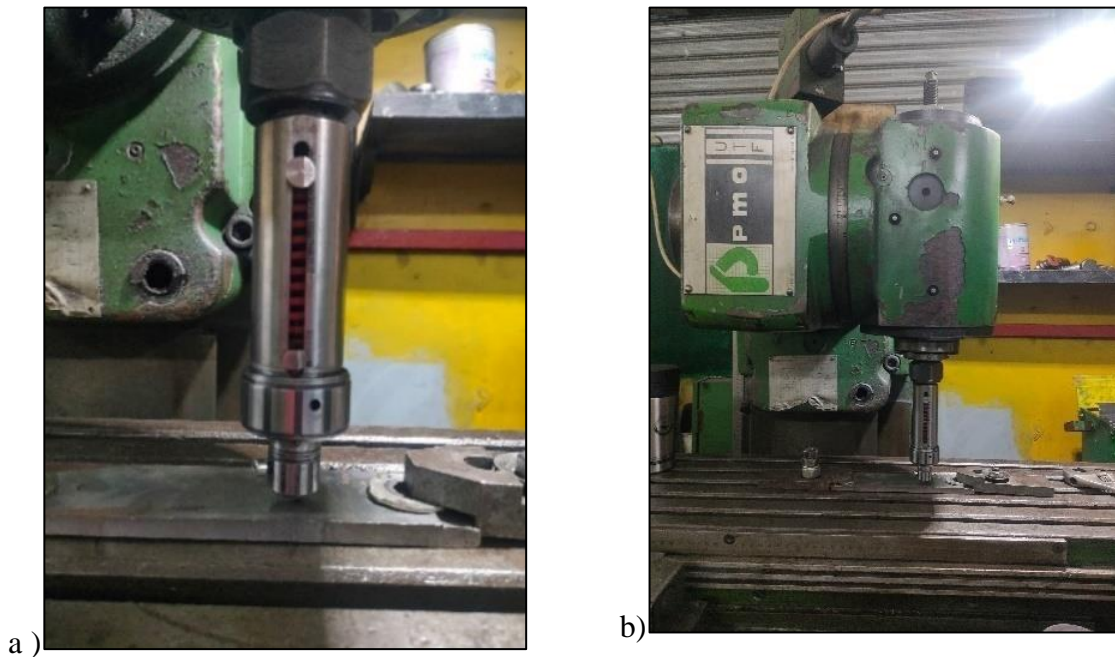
Montage du dispositif de brunissage et de la pièce sur la machine a) Montage du dispositif, b) Fraiseuse verticale PMO
